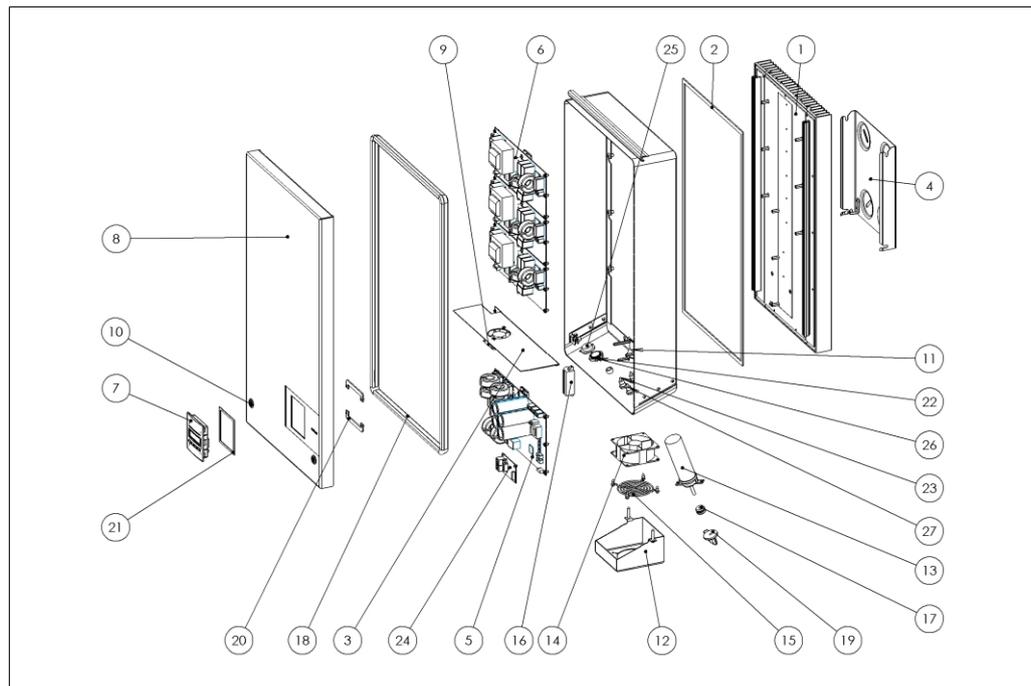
Explosionszeichnung des ULX 5400o
